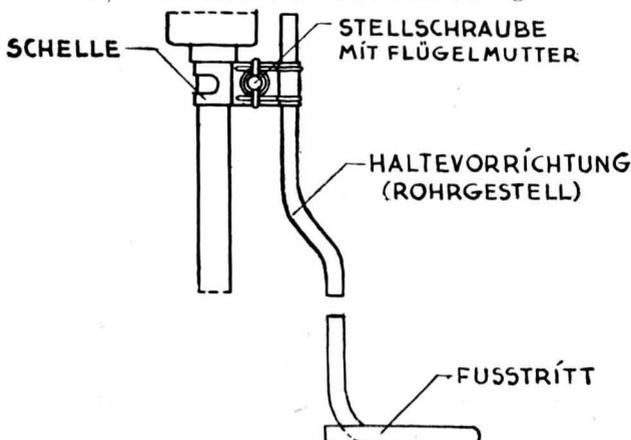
Ausbildung und Befestigung der Haltevorrichtung am Pumpwerk.
